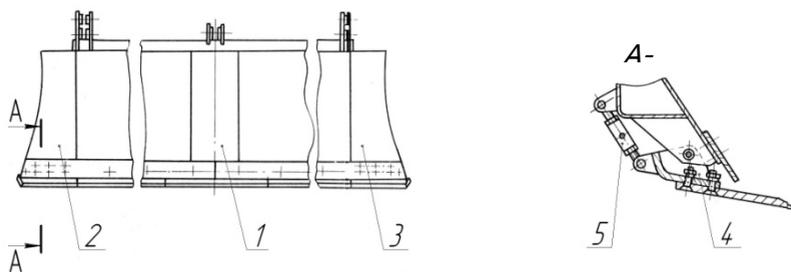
Рабочий орган кустореза МП-14: 1 – отвал; 2, 3 – уширители; 4 – устройство ножевое; 5 – стяжка регулировочная
